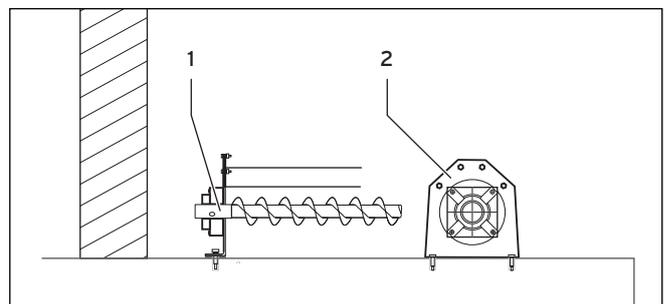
Sección longitudinal del rodamiento con soporte embreado
